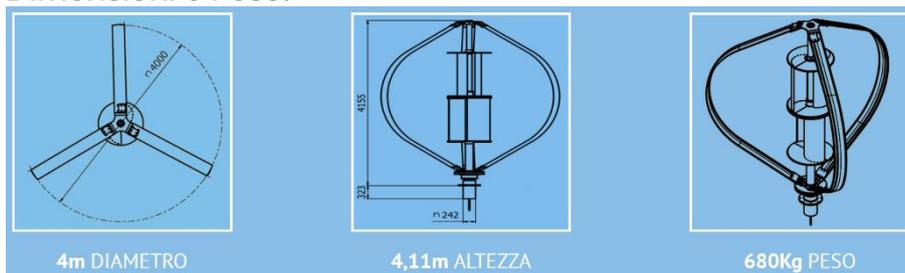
Schema dimensioni e peso della turbina DS3000, etneo.com
